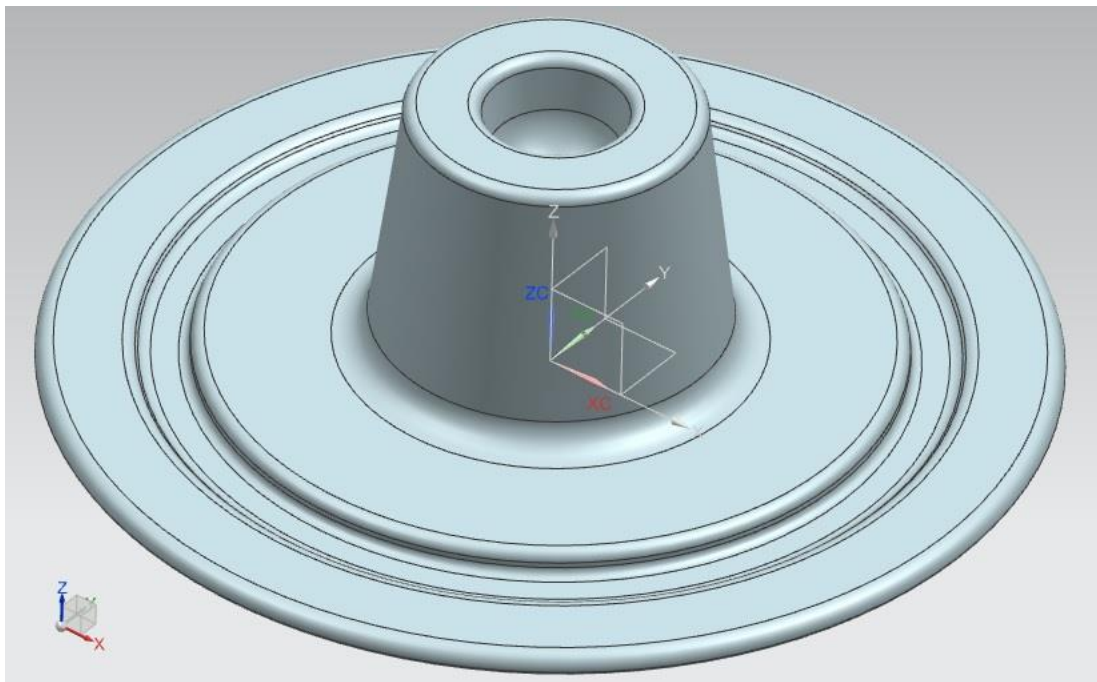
3D-модель гарячої заготовки деталі «Кришка» з додаванням геометрії облойного рівчака I типу
